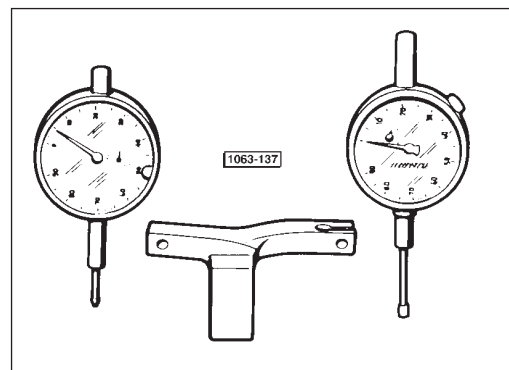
Outil réf. 5.9030.616.4 permettant le calage du moteur.
